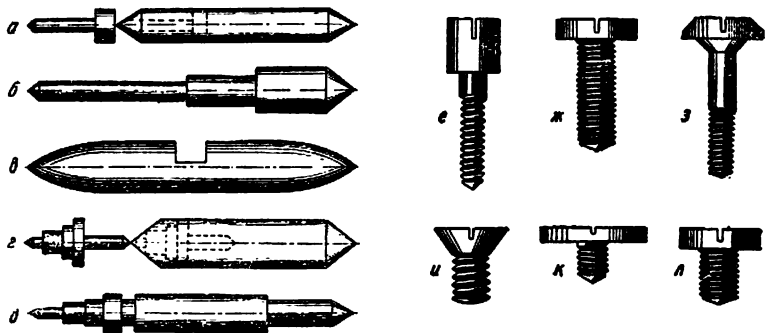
Детали для точения: а — заготовка подавки; б — ось анкера; в — ось будильника; г — заготовка оси баланса; д — ремонтурный вал; е — винт для мостов; ж, з — винты для крепления механизмов; и — винт для пружин; к, л — винты для коронных и барабанных (заводных) колес
